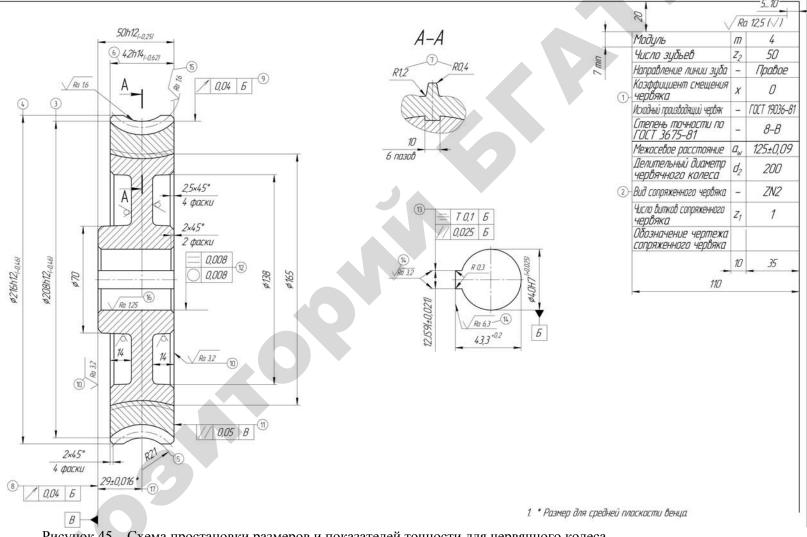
Схема простановки размеров и показателей точности для червячного колеса
